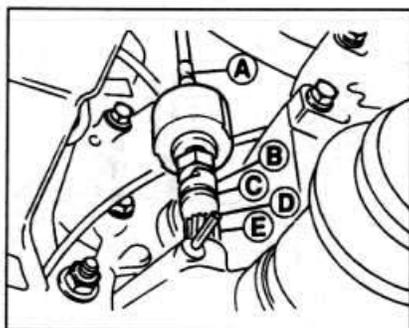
В.6. Расположение троса привода спидометра на автоматической коробке передач.
